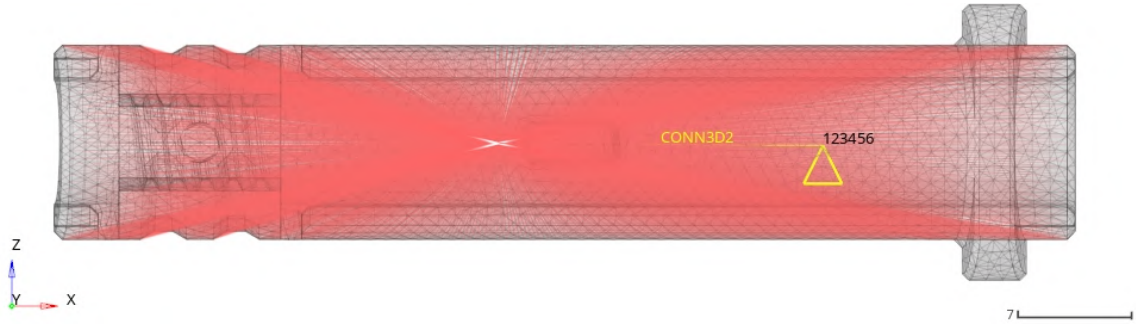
Geometrie šroubu a kompenzátoru
